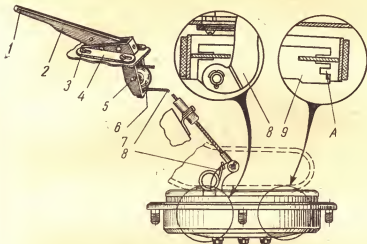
Ручной привод тормоза ЗАЗ-966.
